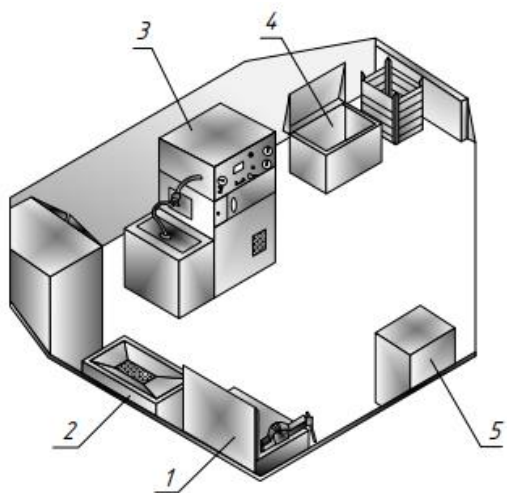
Участок текущего ремонта гидроагрегатов: 1 – верстак слесарный с настольным гидравлическим прессом; 2 – ванна моечная передвижная; 3 – универсальный стенд для испытания и регулировки гидроагрегатов; 4 – верстак слесарный с комплектом оснастки для текущего ремонта гидроагрегатов; 5 – установка для очистки масел; стенды для испытания агрегатов гидростатических трансмиссий и гидроусилителей рулевого управления не обозначены
